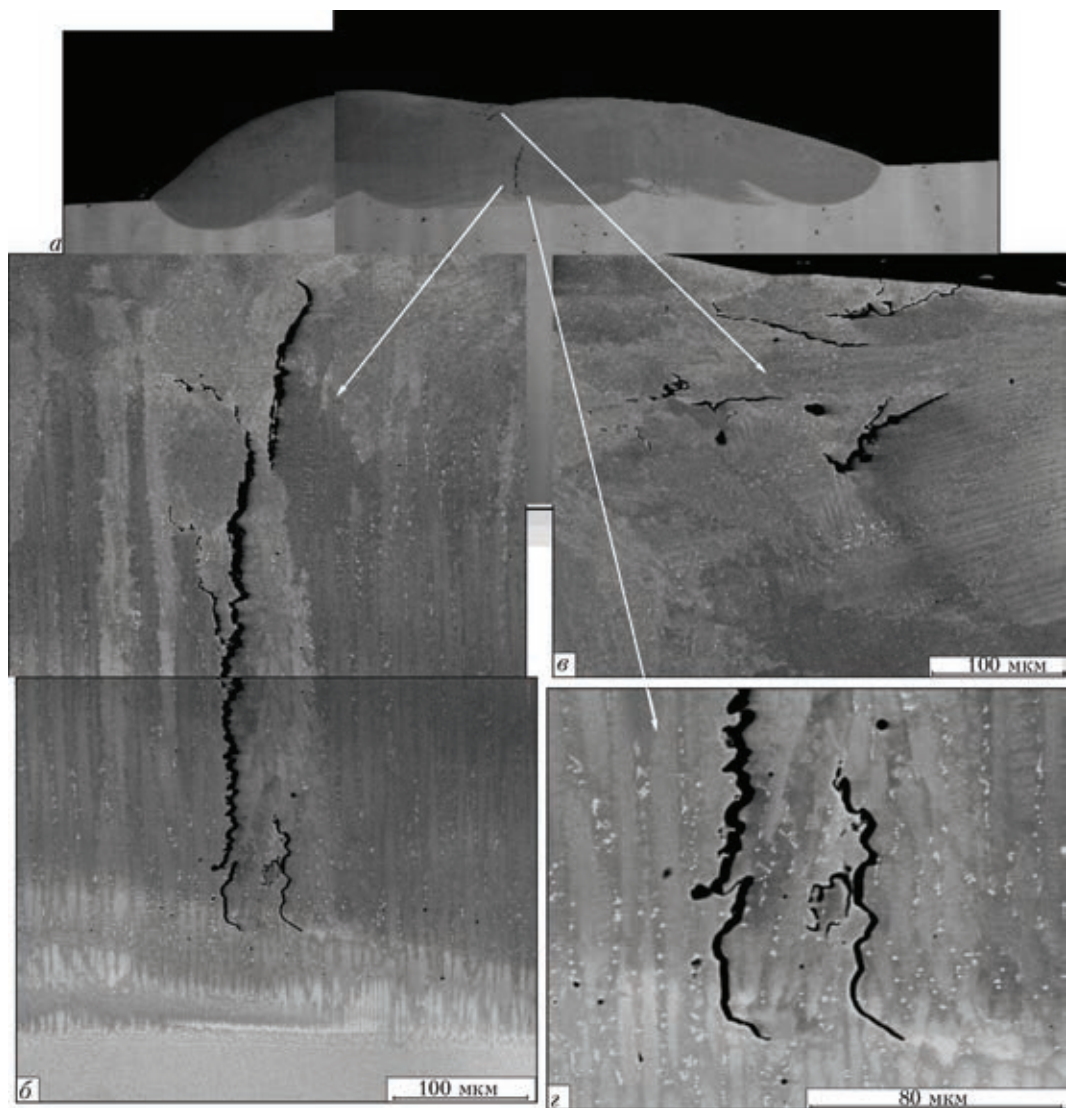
Кристаллизационные межзеренные трещины в металле двухпроходного шва, сформированного с применением присадочного материала IN738 на сплаве CMSX-4: *a* — общий вид шва; *б, в* — трещины в центре и на поверхности шва; *г* — вершина шва
